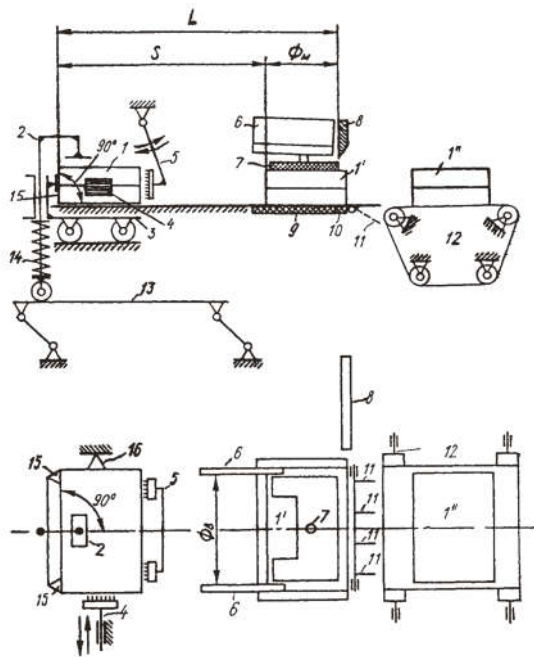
Принципова технологічна схема машини трьохножової для різання паперових заготовок (однопозиційної): 1 - блоки; 2 - система попереднього притискання; 3 - піддавач заготовок; 4 - підштовхувач заготовок; 5 - щітки; 6 - ножі бічні; 7 - головна система притискання; 8 - ніж передньої частини; 9 і 10 - упори ножів; 11 - хитний місток; 12 - транспортер відводу заготовки; 13 - планка керування; 14 - пружина; 15 - упор задній; 16 - упор бічний
